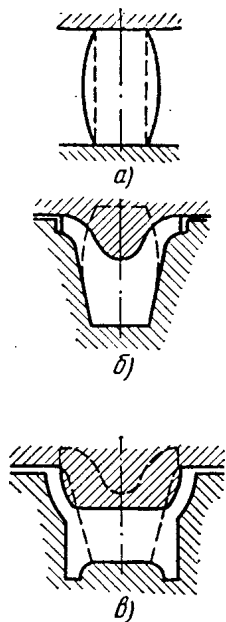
Последовательность изготовления штамповкой сплошной детали типа тела вращения:
